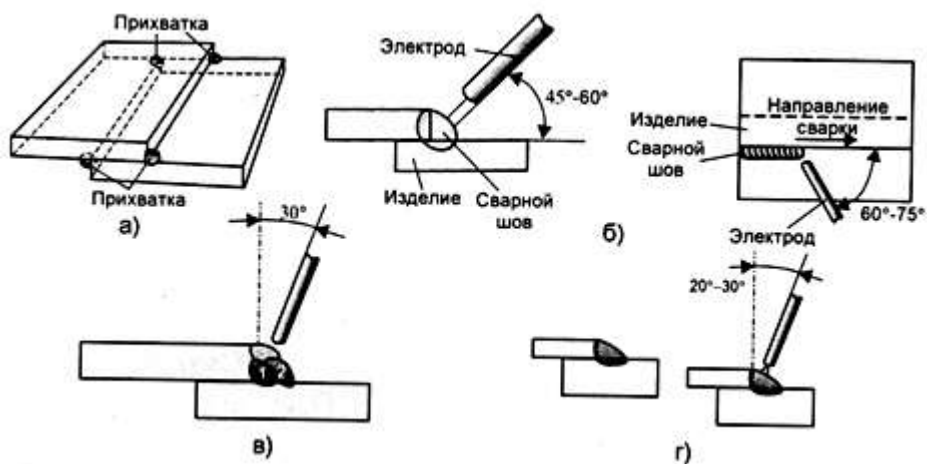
Сварка нахлесточного соединения в нижнем положении.
